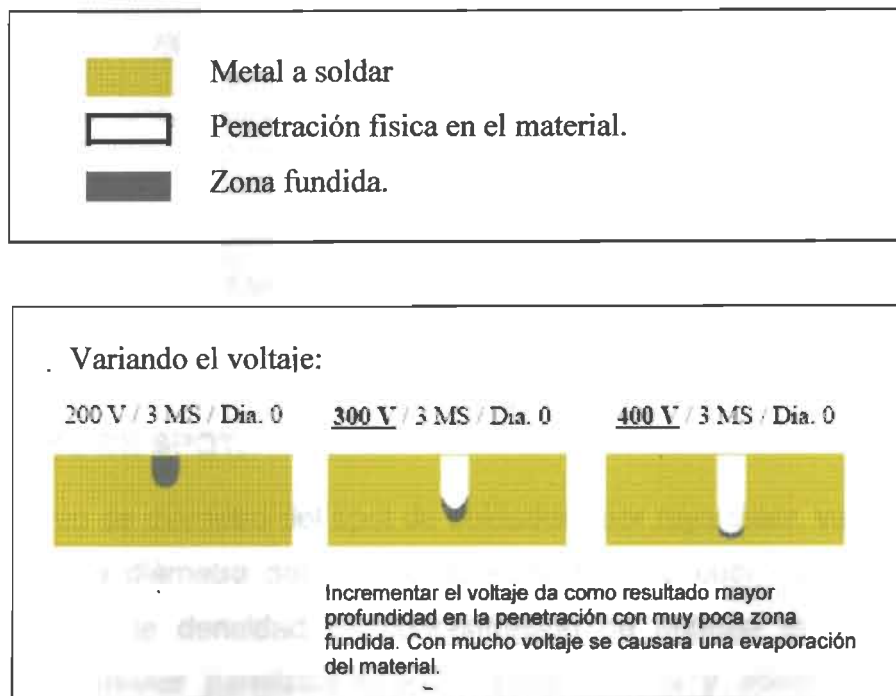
Efecto del voltaje en la soldadura láser.
